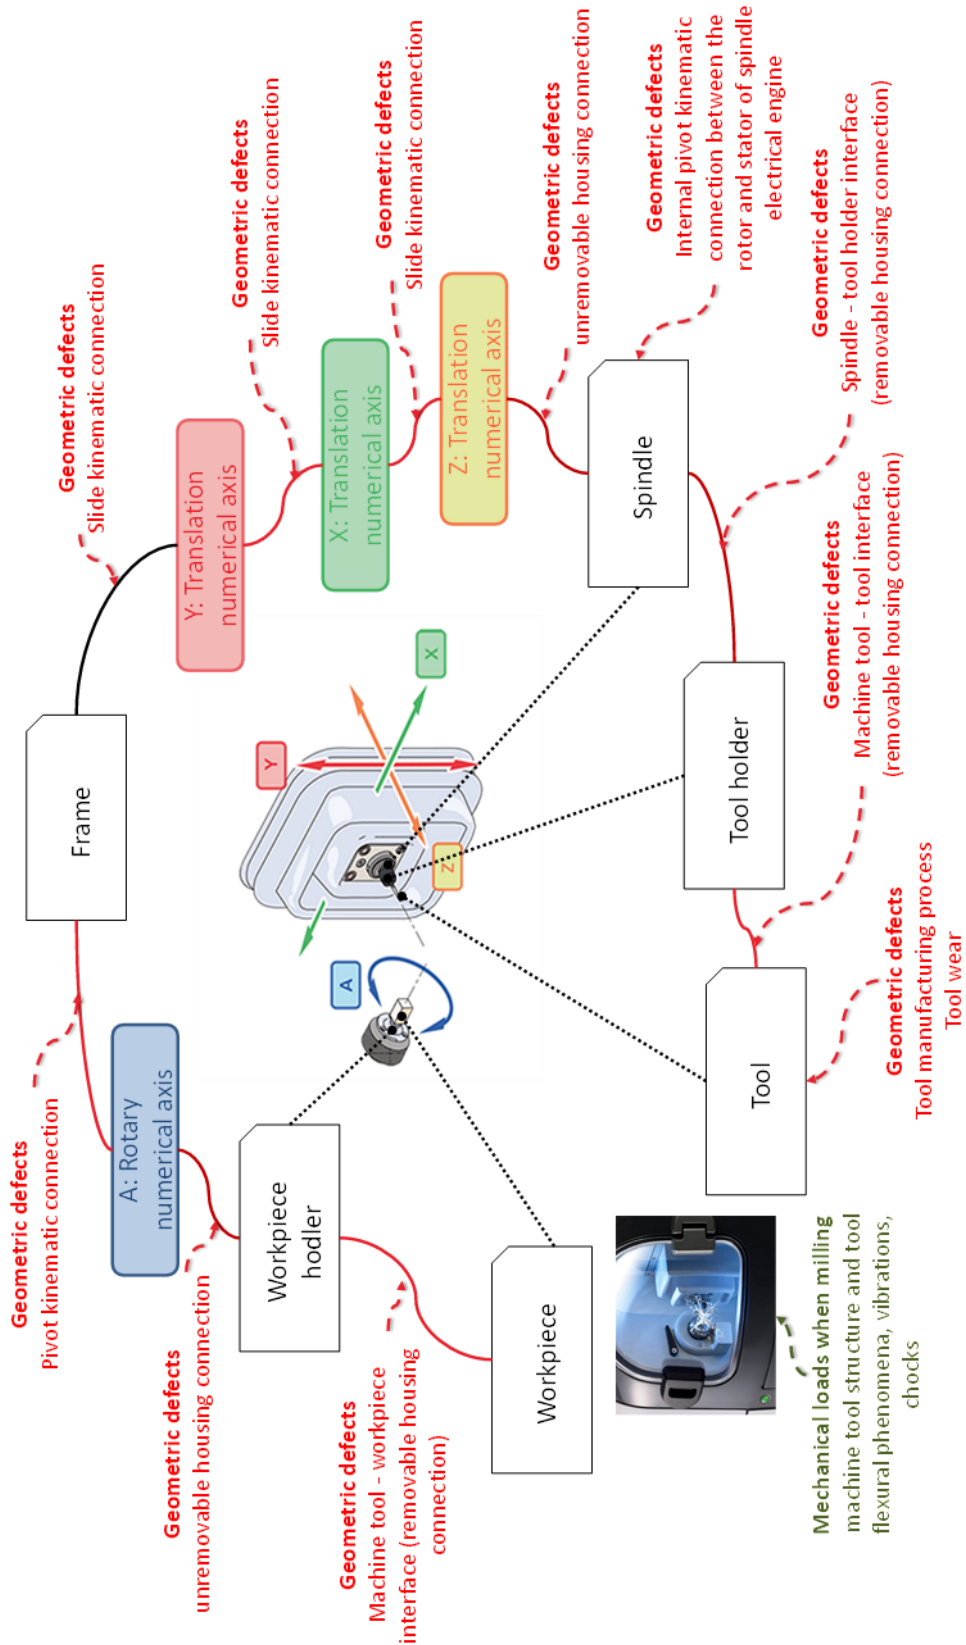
Structure d'une machine-outil : sources de dispersions géométriques (exemple basé sur la machine-outil Carestream CS 3000, Carestream dental [New York, USA])
